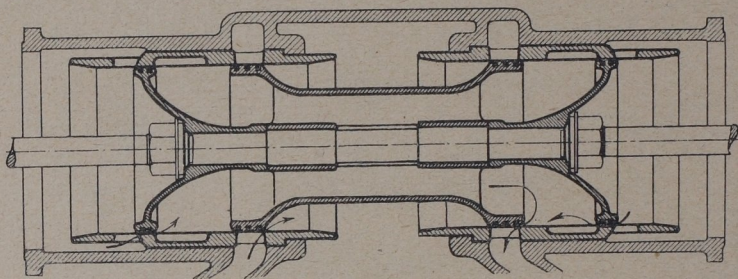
Kammerschieber Bauart „Hochwald“ für Niederdruckzylinder, mit äußerer Einströmung.
